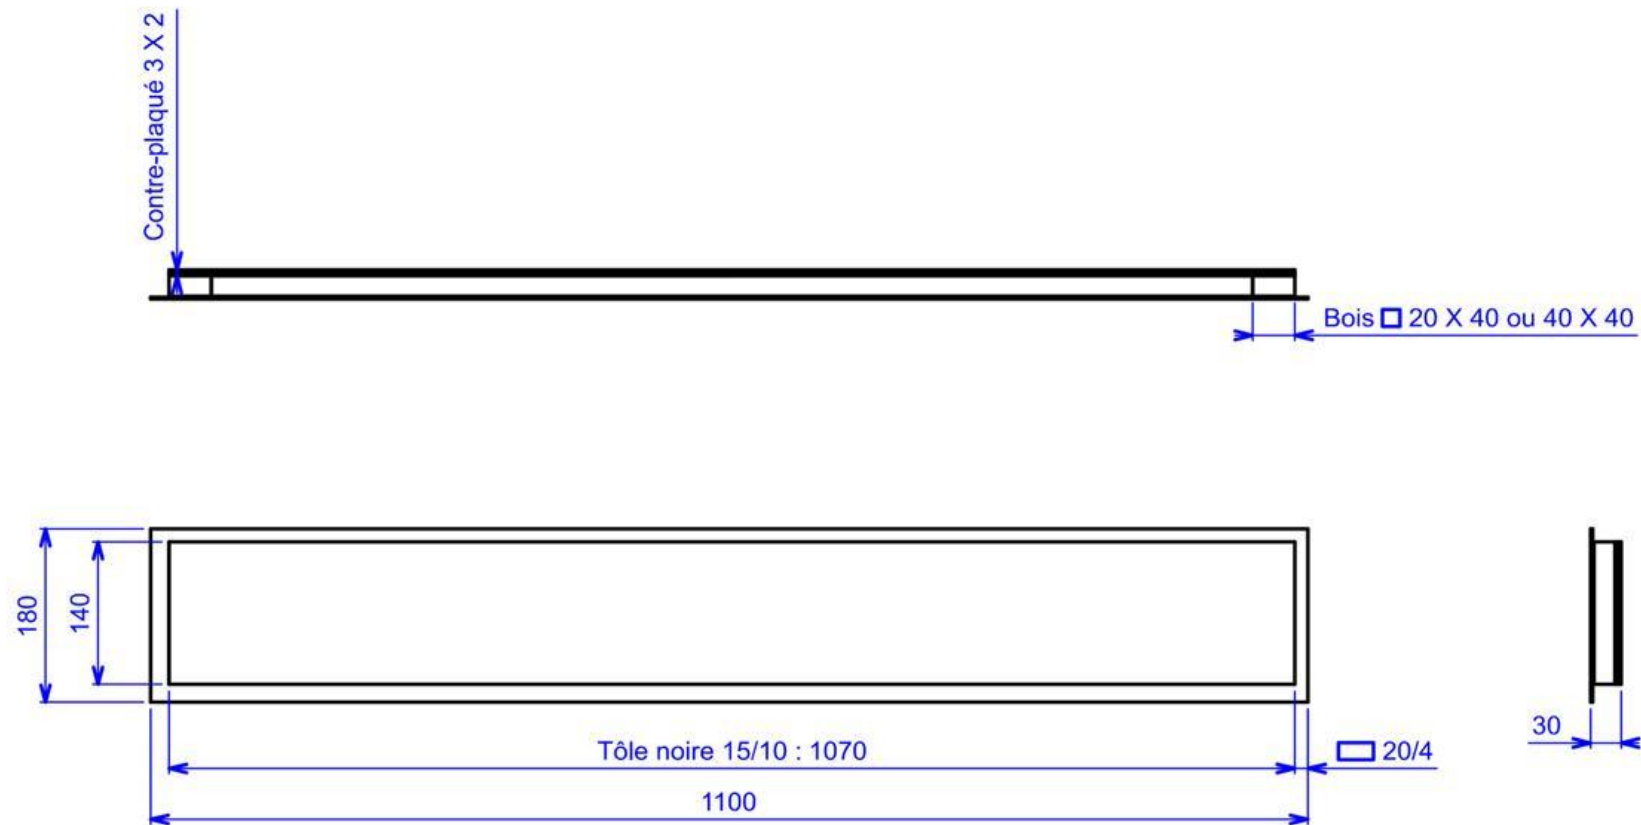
Dessin de définition de la chambre du brûleur de gaz
